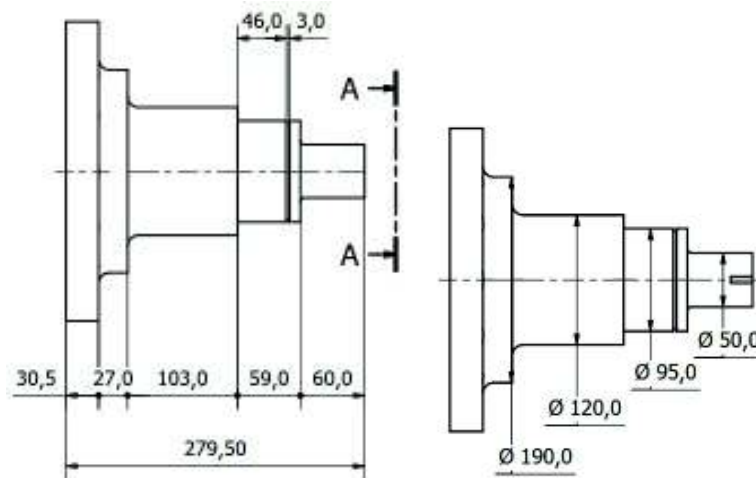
Dimensiones del eje principal del sistema de arranque
